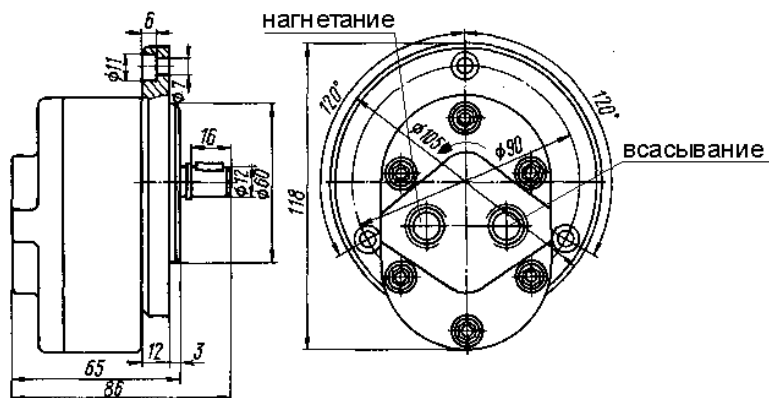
Габаритные и присоединительные размеры насоса типа АГ11-1
